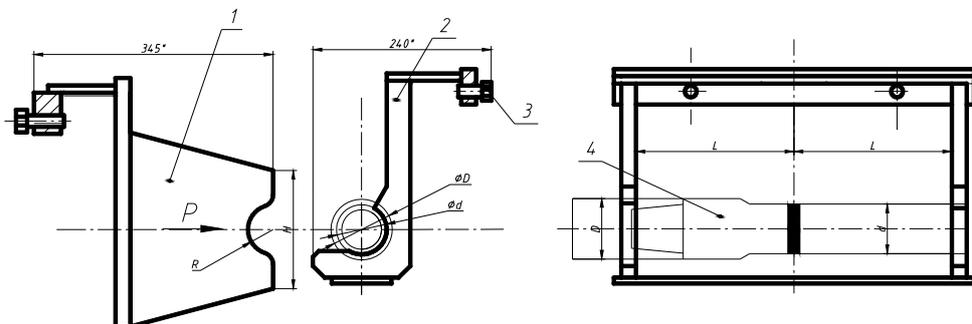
Приставка к разрывной машине ДЗБО для испытания труб на изгиб
